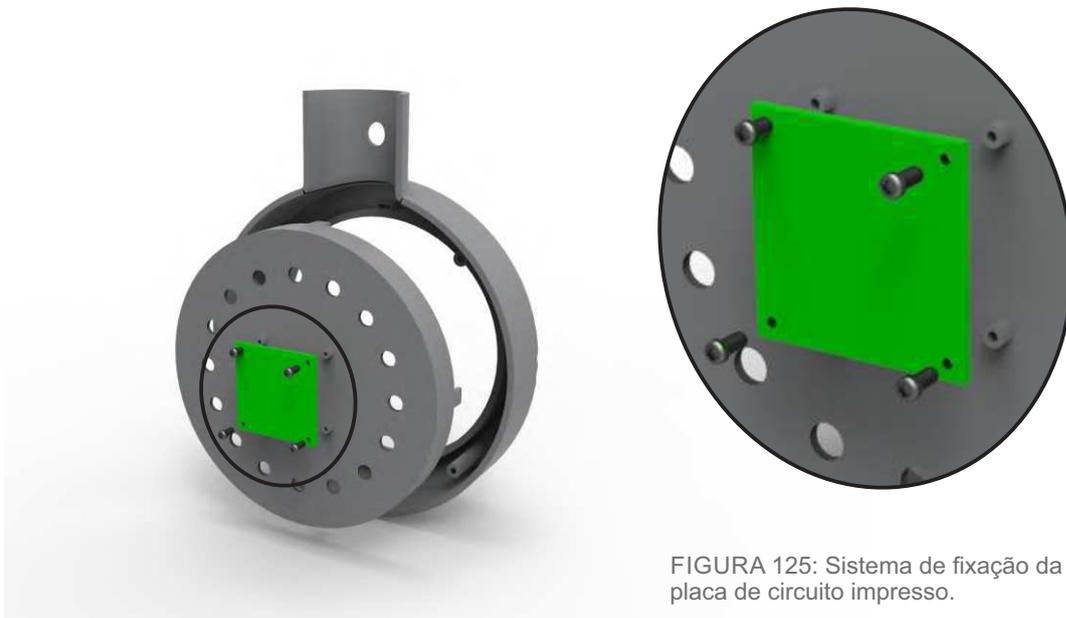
Sistema de fixação da placa de circuito impresso.
